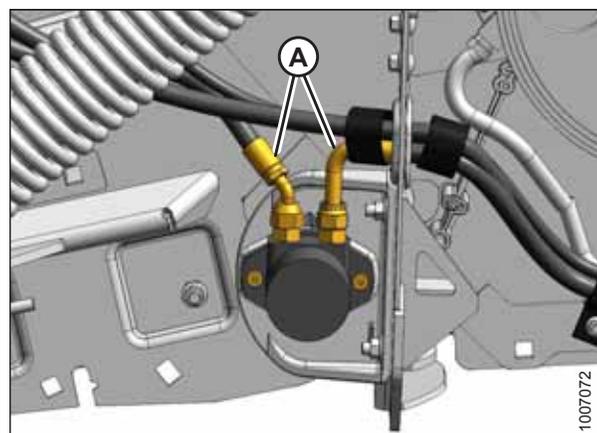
Motor hidráulico trasero; lado izquierdo
